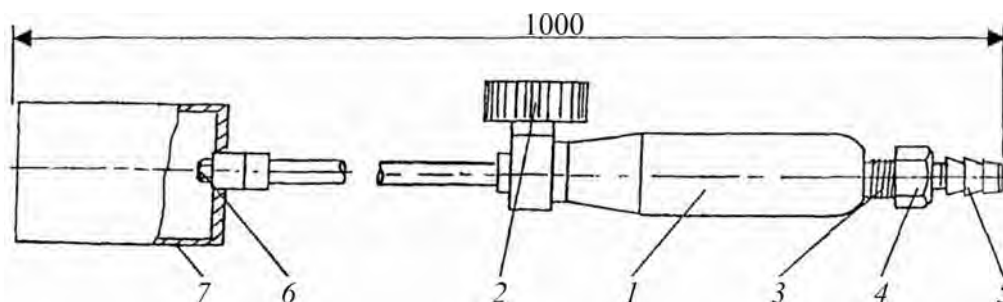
Горелка газоздушная ГВ-1-02П: 1 — ствол с рукояткой; 2 — регулировочный вентиль; 3 — штуцер; 4 — накидная гайка; 5 — ниппель; 6 — инжектор (сопло); 7 — стакан
